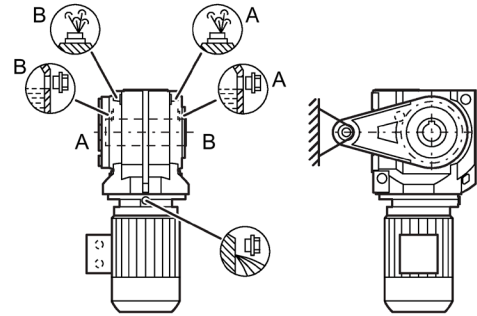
Einbaulagen für Stirnradschneckengetriebe CAD Aufsteckausführung Baugröße 39A
